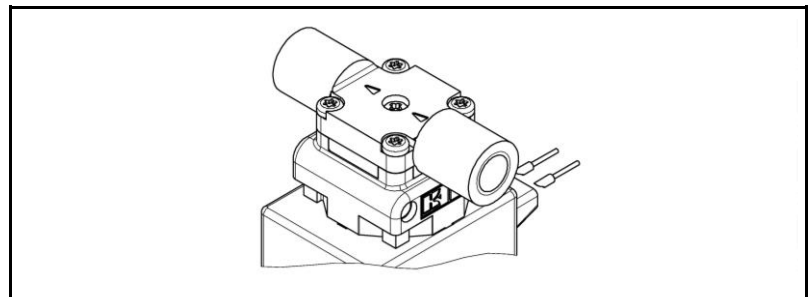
Pumpenkopf mit UNF-1/4“-Gewinde-Anschluss
